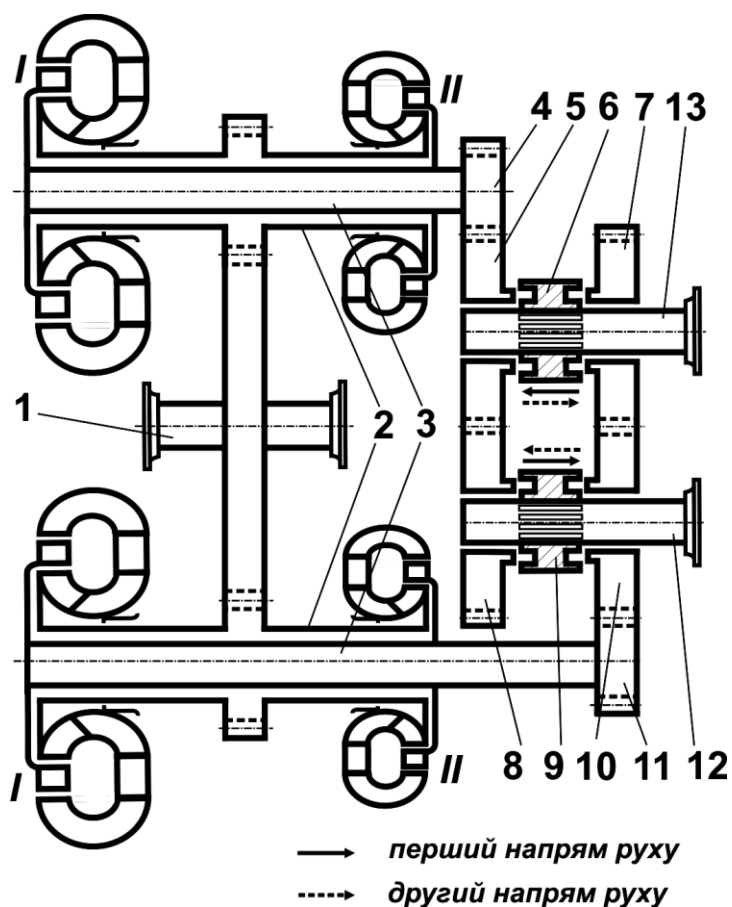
Схема багатопотокової БГП із шістьма реверсивними шестірнями:
